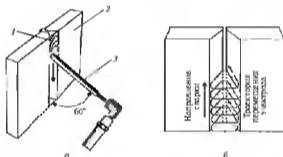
Сварка стыкового соединения со скосом кромок сверху вниз (а) и траектория перемещения электрода при однопроходной сварке с поперечными колебаниями (б):
